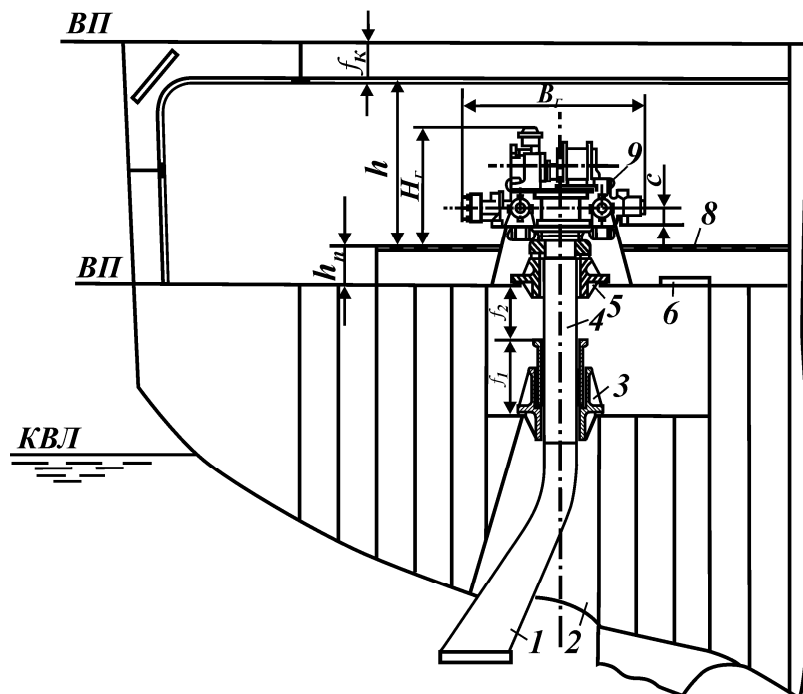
Компоновка деталей рулевого устройства с изогнутым баллером.
